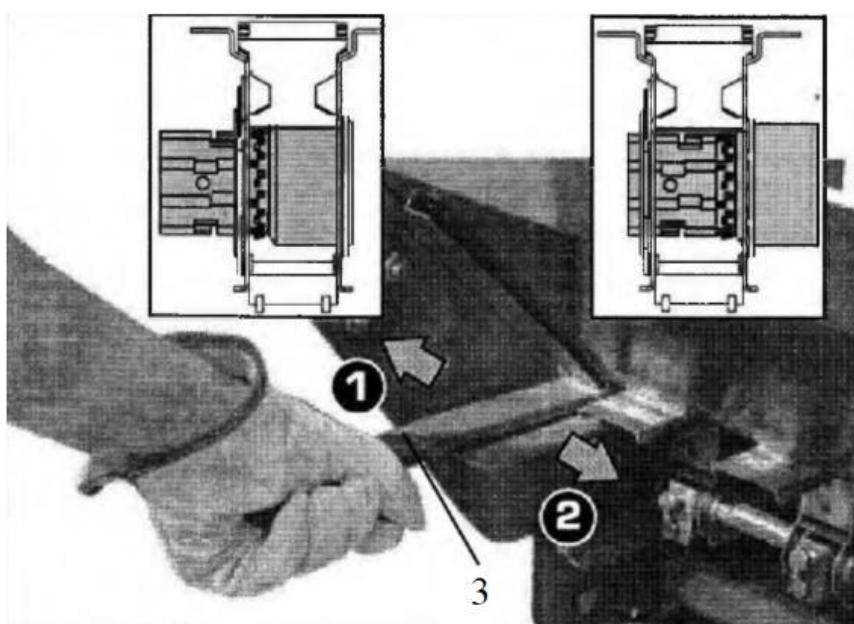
Устройство высевашего аппарата сеялки ЗС-6: 1 – положение для высева мелкосеменных культур; 2 – положение для высева семян зерновых и зернобобовых; 3 – ручка регулировки положения катушки
